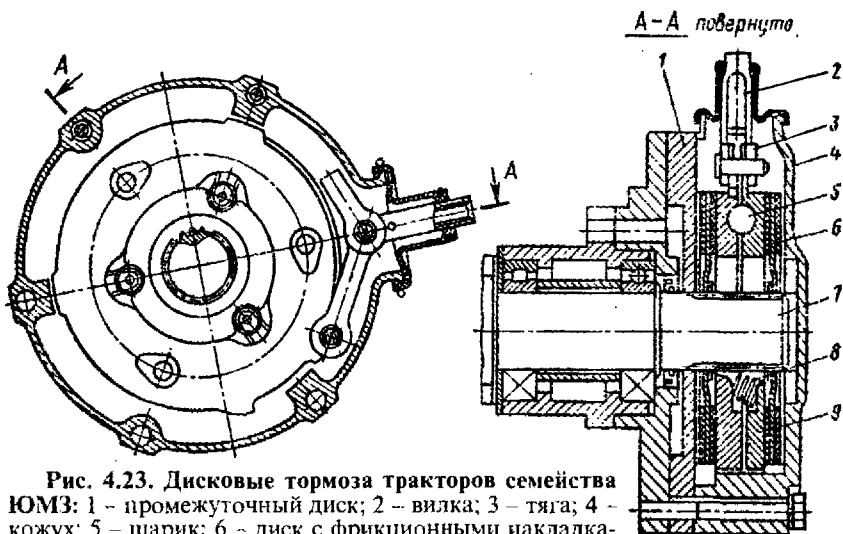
Дисковые тормоза тракторов семейства ЮМЗ: 1 - промежуточный диск; 2 - вилка; 3 - тяга; 4 - кожух; 5 - шарик; 6 - диск с фрикционными накладками; 7 - ведущий вал; 8 - пружина; 9 - тормозные диски
